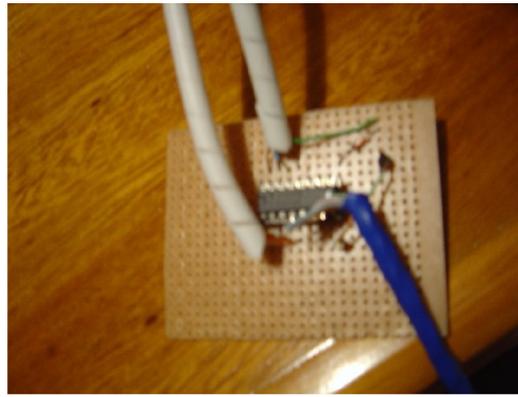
Placa que faz a comunicação entre a porta paralela e o motor com cabos
